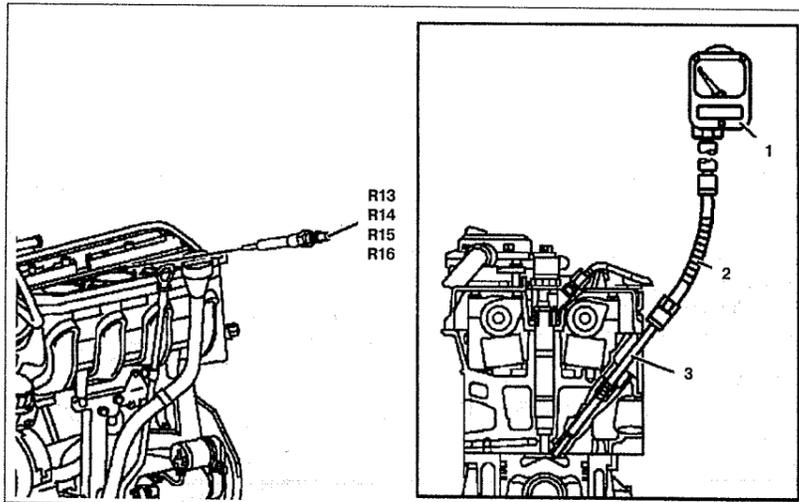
Проверка компрессии двигателя: 1. Компрессометр, 2. Переходник, 3. Резьбовой переходник, R13-R16. Свечи накаливания.
